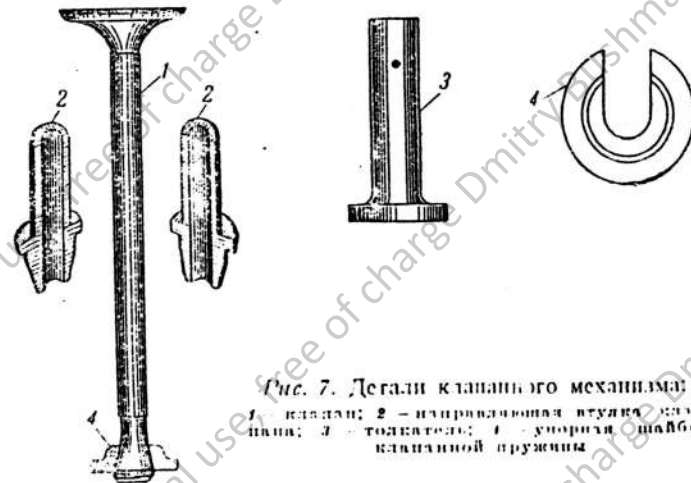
Детали клапанного механизма: 1 — клапан; 2 — направляющая втулка клапана; 3 — толкатель; 4 — устройство шайба клапанной пружины
